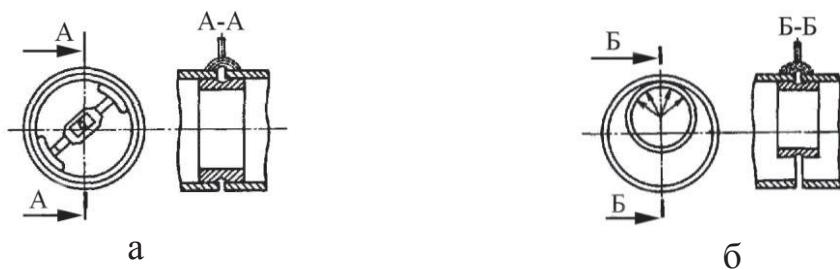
Флюсомедные подкладки для сварки кольцевых швов
